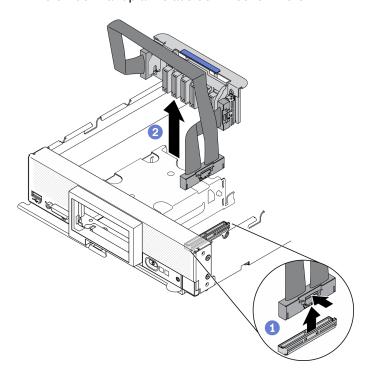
Entfernen der Rückwandplatinenbaugruppe für EDSFF-Laufwerke
